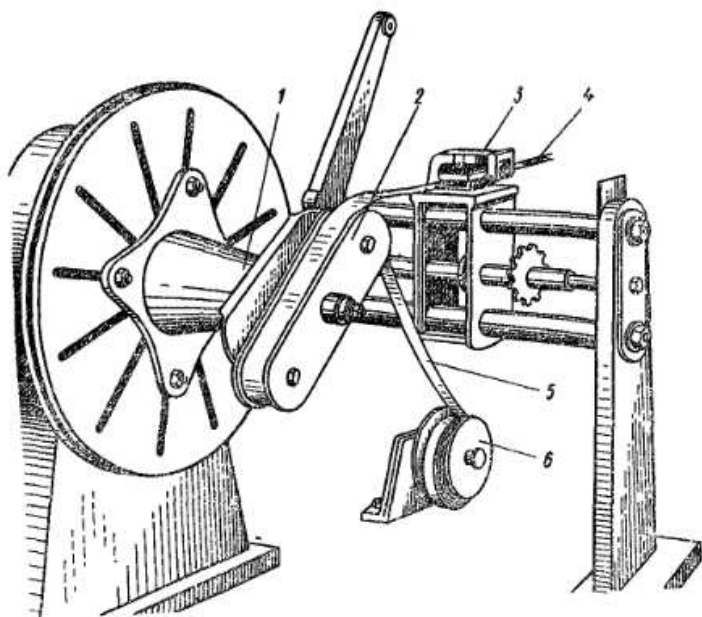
Станок для намотки катушек из шинной меди плашмя
